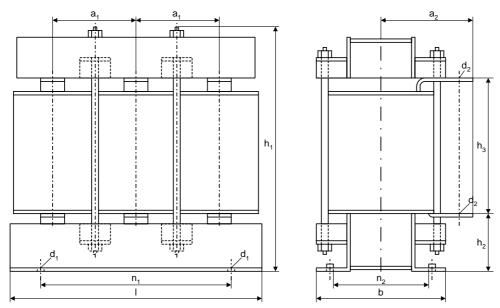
Disegni d'ingombro delle bobine AFE
